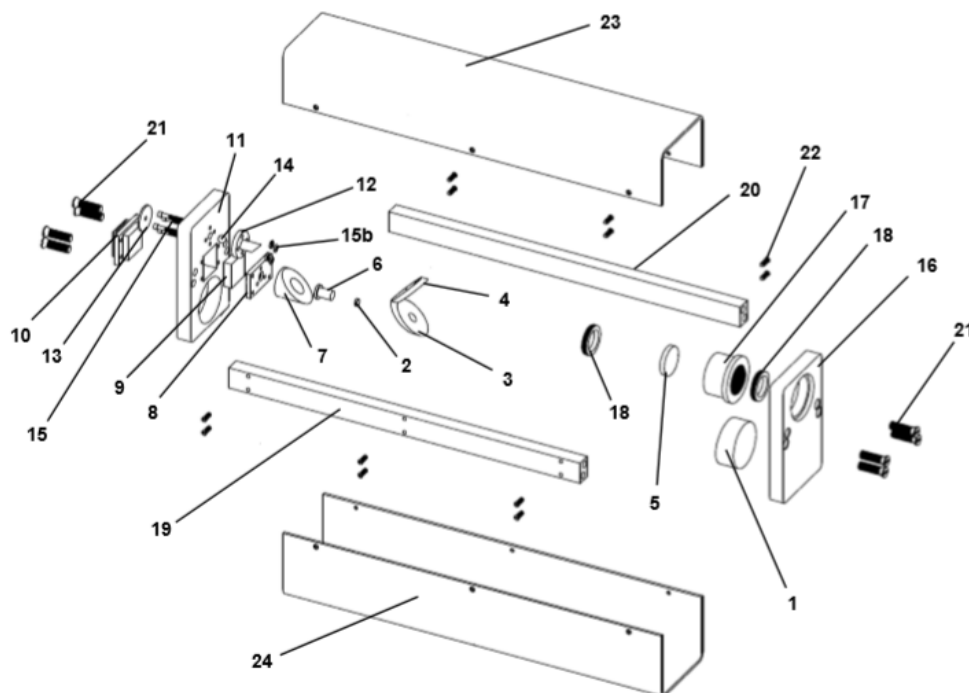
Vista en explosión de componentes ópticos y mecánicos del radiómetro [22].
